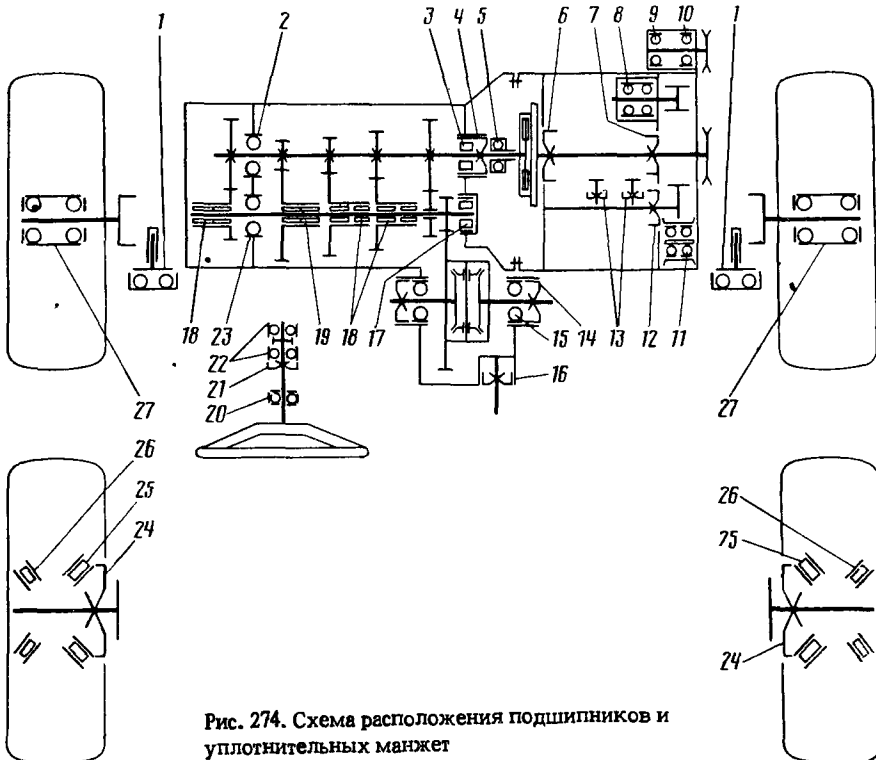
Схема расположения подшипников и уплотнительных манжет
